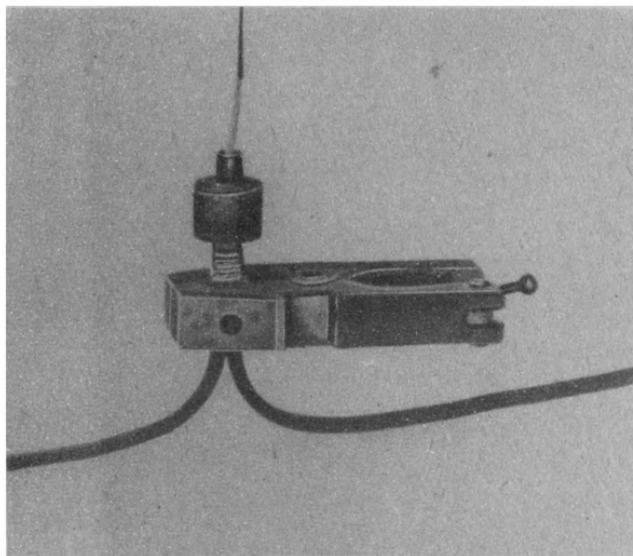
Патрон марки АС с охладителем, установленный для сварки ответвленного провода
